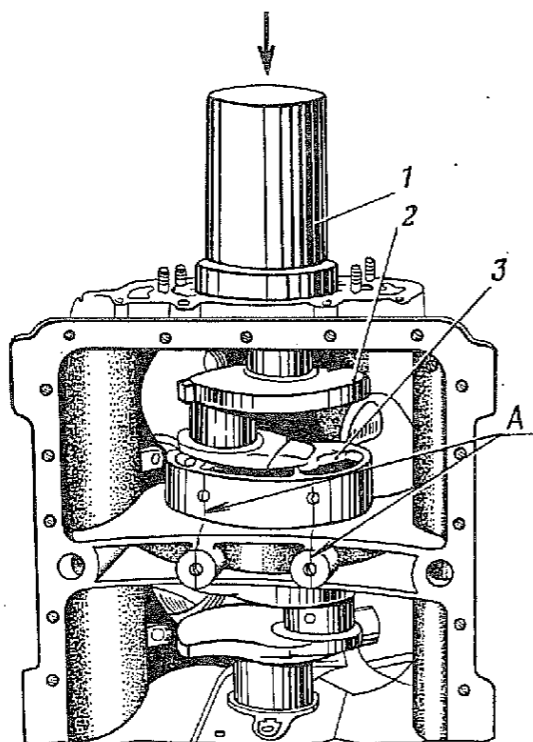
Запрессовка средней опоры в сборе с коленчатым валом в картер:
